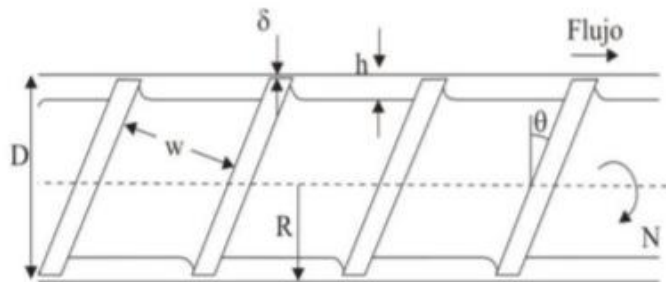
Partes diferenciadas de una boquilla de extrusión [53].
